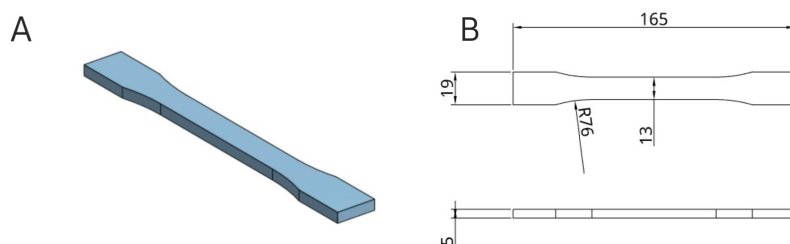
Modelo do corpo de prova: (A) vista em perspectiva do modelo 3D; (B) desenho técnico com dimensões conforme a norma ASTM D638-22.
